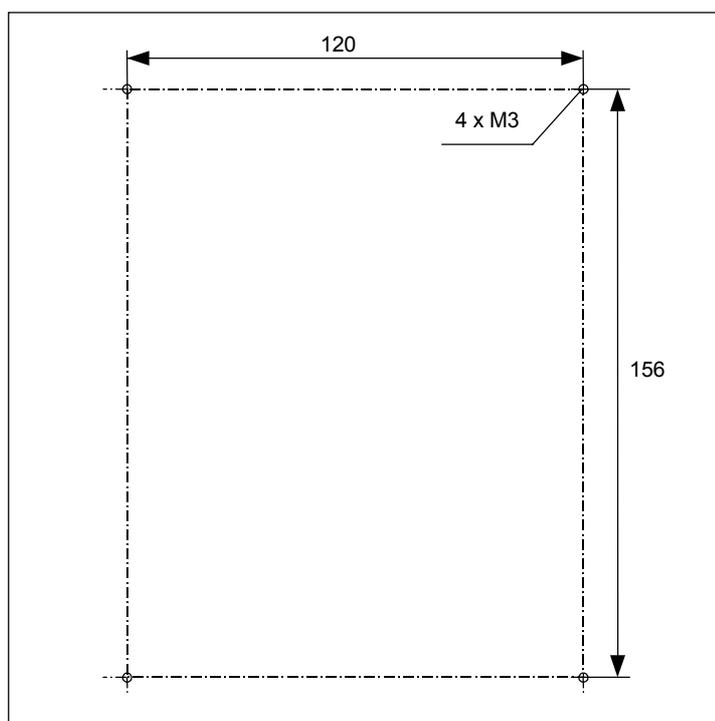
Maße des Bohrbildes für den Schrankeinbau
